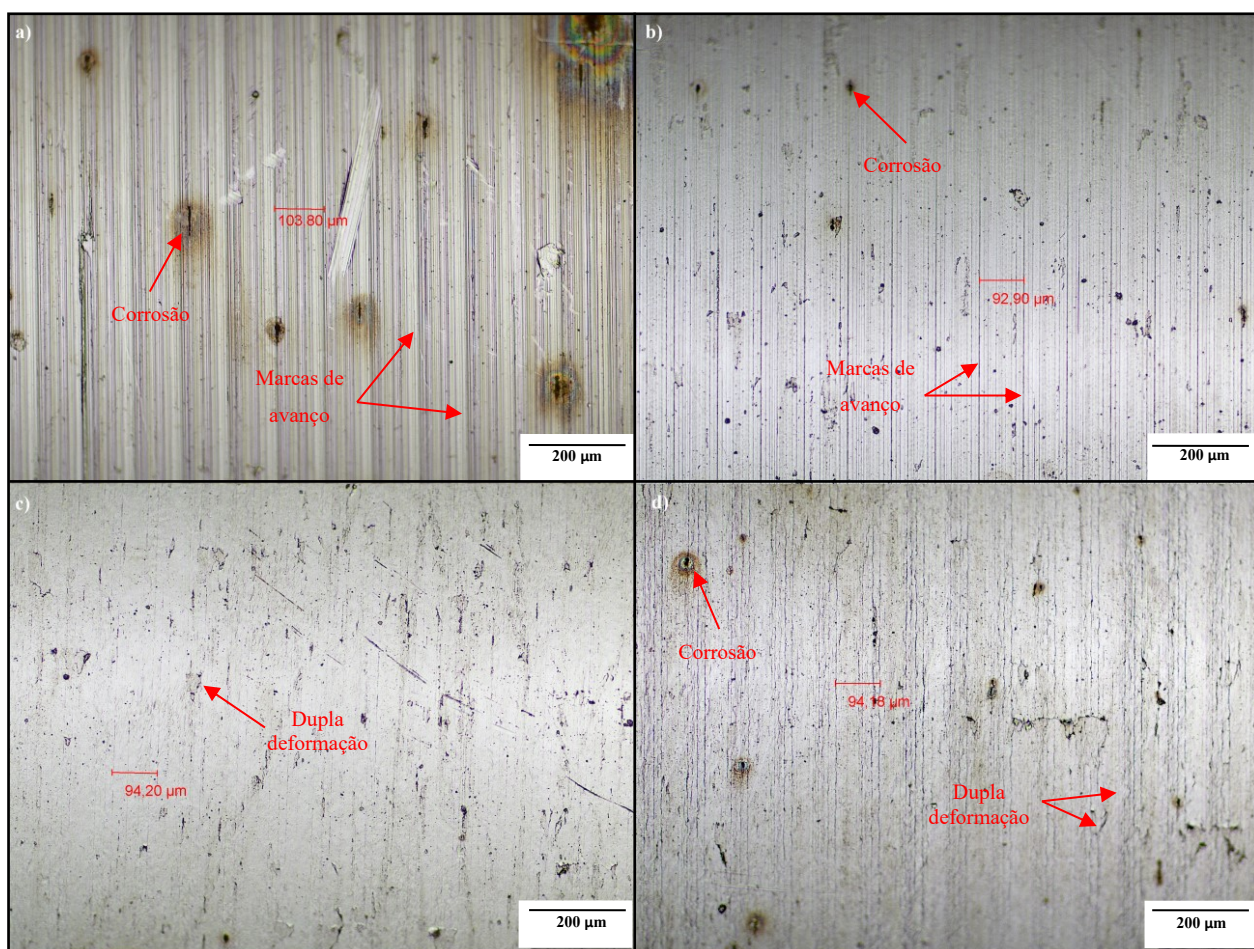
Microscopia ótica das superfícies: a) torneada, b) roleteada com  $P_r = 100$  bar,  $V_r = 30$  m/min e  $f_r = 0,09$  mm/volta, c) roleteada com  $P_r = 200$  bar,  $V_r = 30$  m/min e  $f_r = 0,09$  mm/volta, e d) roleteada com  $P_r = 300$  bar,  $V_r = 30$  m/min e  $f_r = 0,09$  mm/volta.
